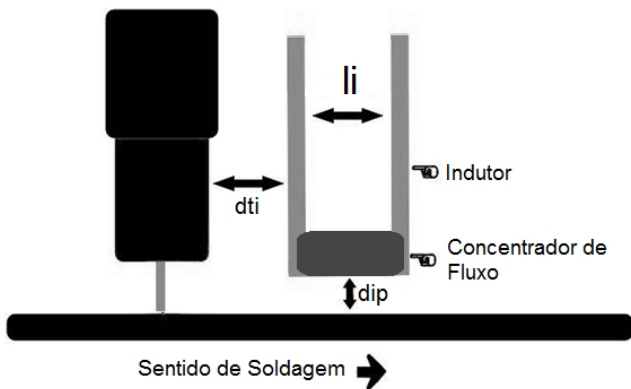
Esquema da montagem em tandem de um sistema de soldagem MIG/MAG com pré-aquecimento indutivo localizado.
